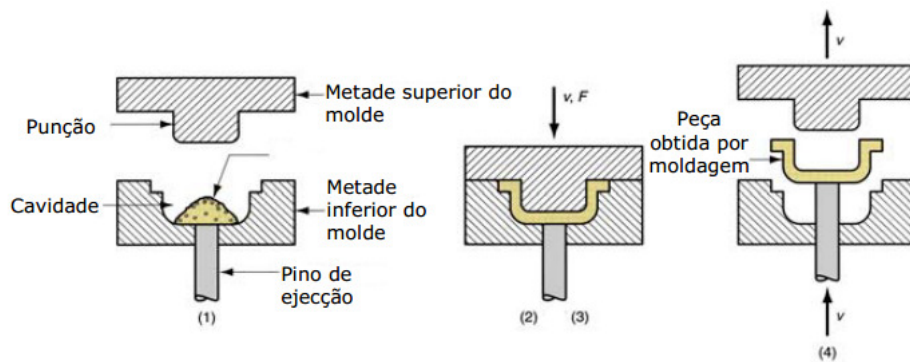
Esquema ilustrativo da moldagem por compressão [8]
